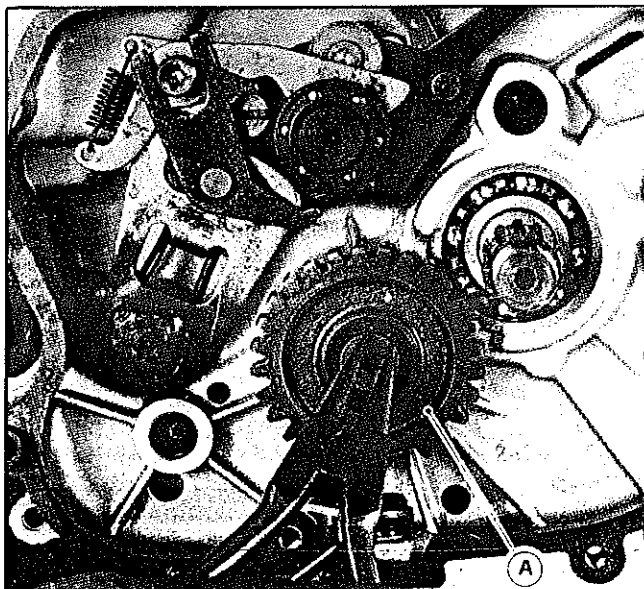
A. ENGRENAGEM INTERM. DO ARRANQUE
